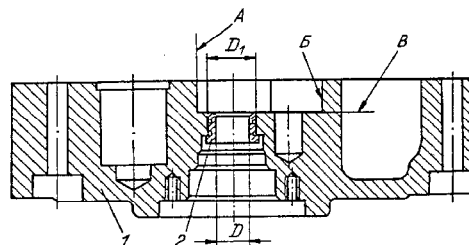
Корпус 2 нижний в сборе /рис. 129/
